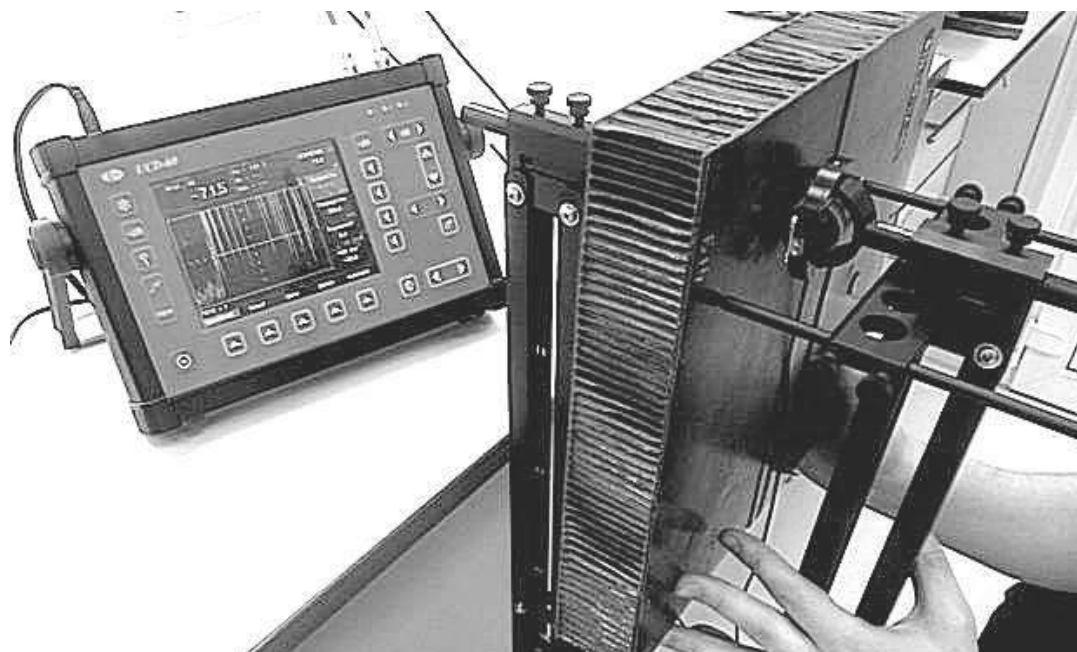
Контроль непроклеювання обшивки до стільникового заповнювача
